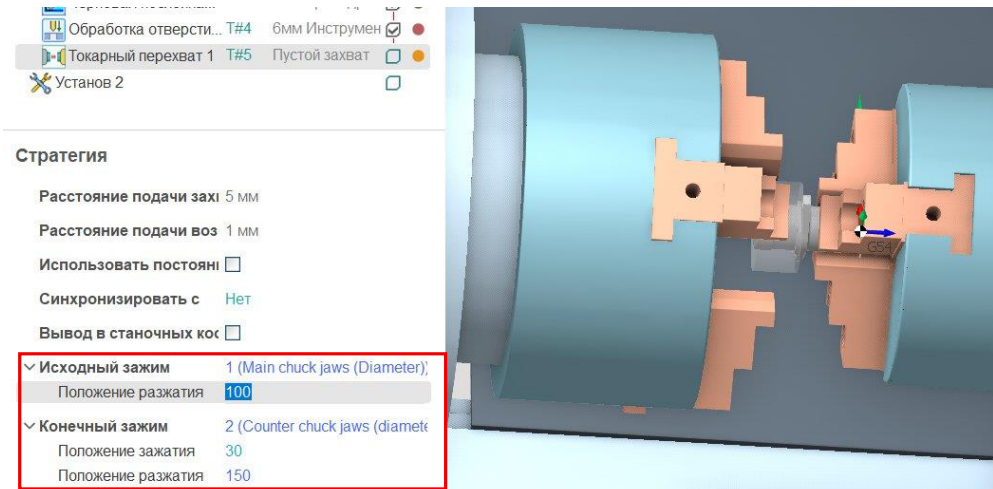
Положение кулачков патронов в операции Токарный перехват.
